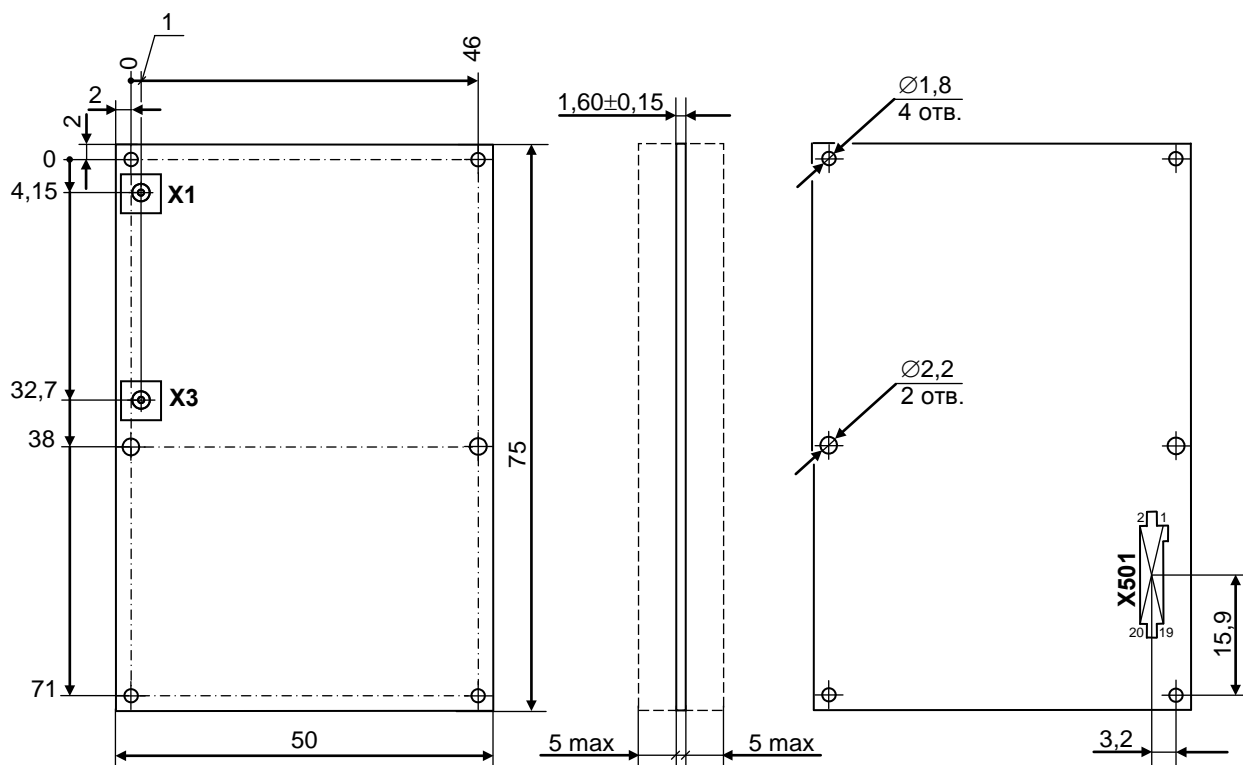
Габаритные и установочные размеры ПН АПМА.468173.002-02
